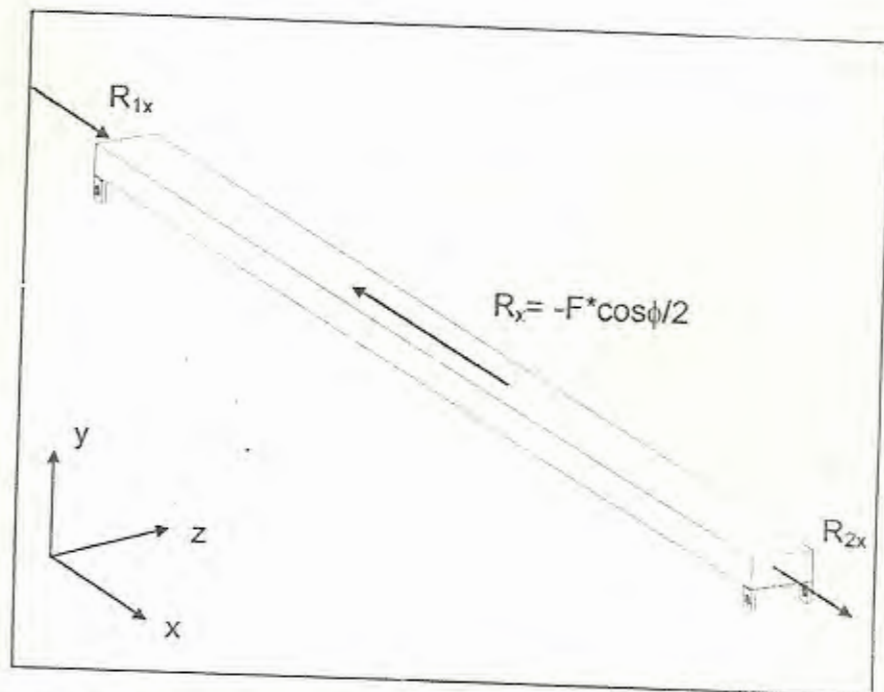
FUERZA R_x APLICADO A VIGA LONGITUDINAL
